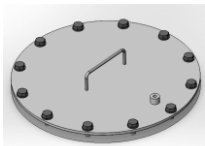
Первое исполнение сборочного узла «Установка заглушки»
